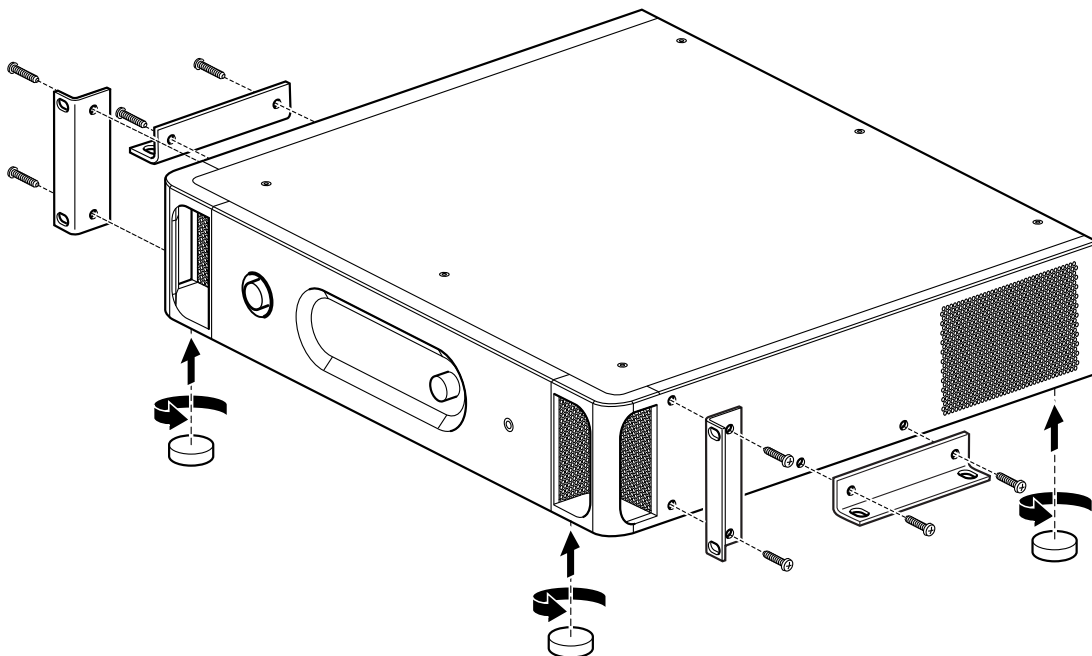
Передатчик с дополнительными монтажными кронштейнами и ножками для установки на столе
